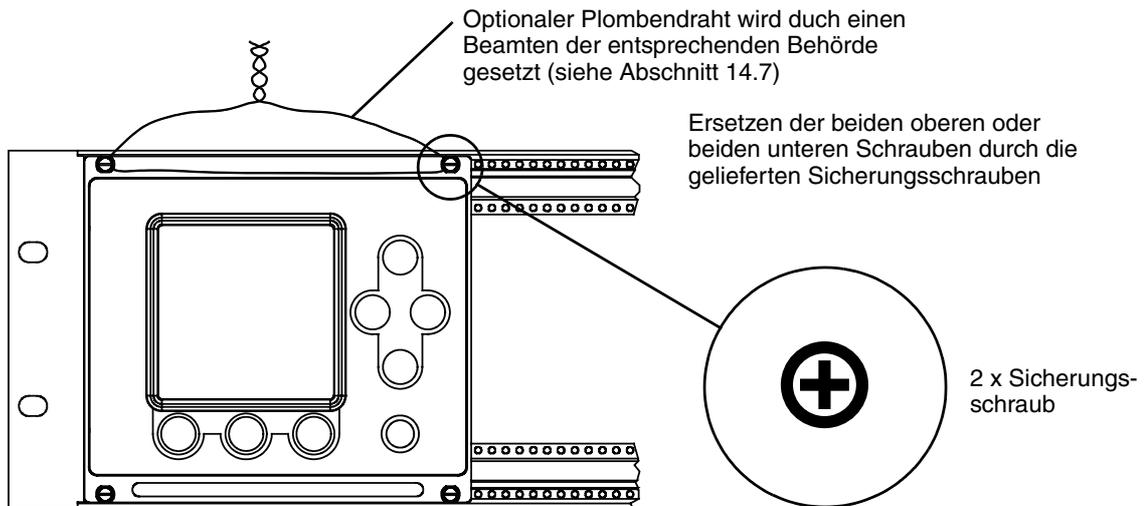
Sicherungsschraube an Geräte in Rackausführung installieren
